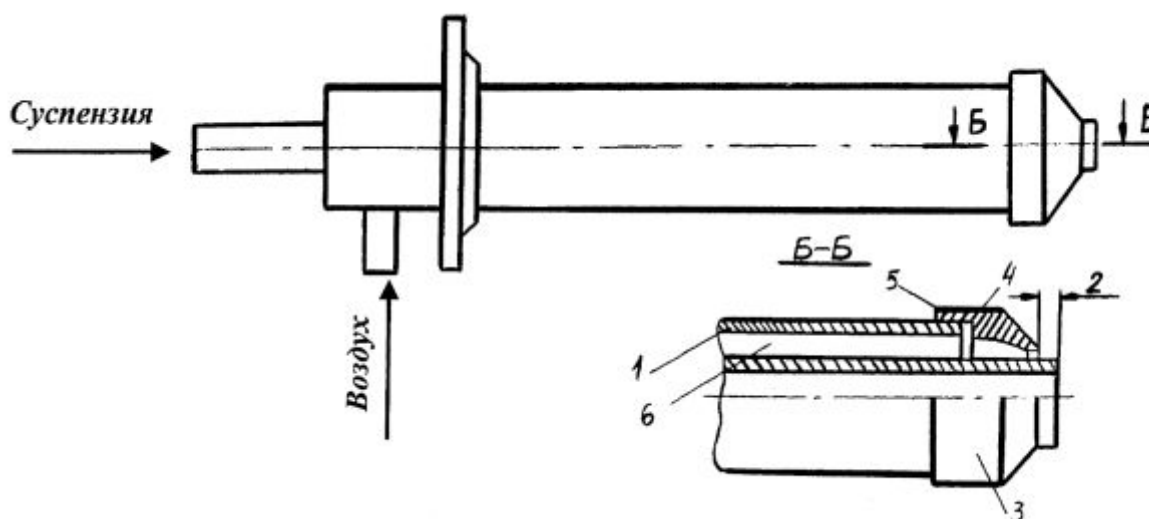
Конструкция пневматической форсунки: 1 – корпус; 2 – патрубок; 3 – втулка; 4 – шайба центровочная; 5 – сопло; 6 – трубка подачи суспензии.
